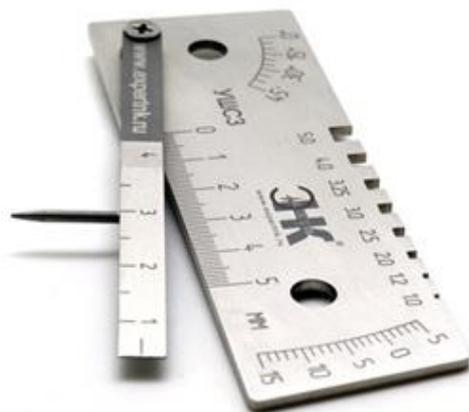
Универсальный шаблон сварщика УШС-3
